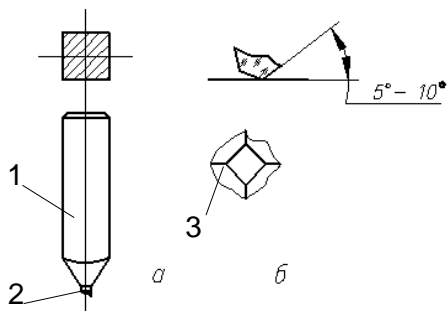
Алмазный резец: а – схематичное представление, б – геометрия заточки: 1 – корпус резца; 2 – алмаз, 3 – ведущая кромка
